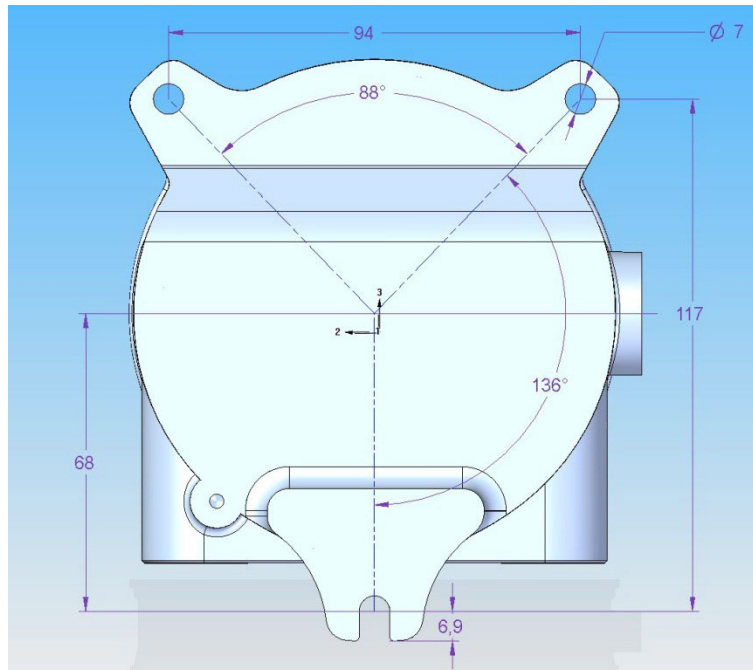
Bohrungsabmessungen für die Befestigung der Halterung
